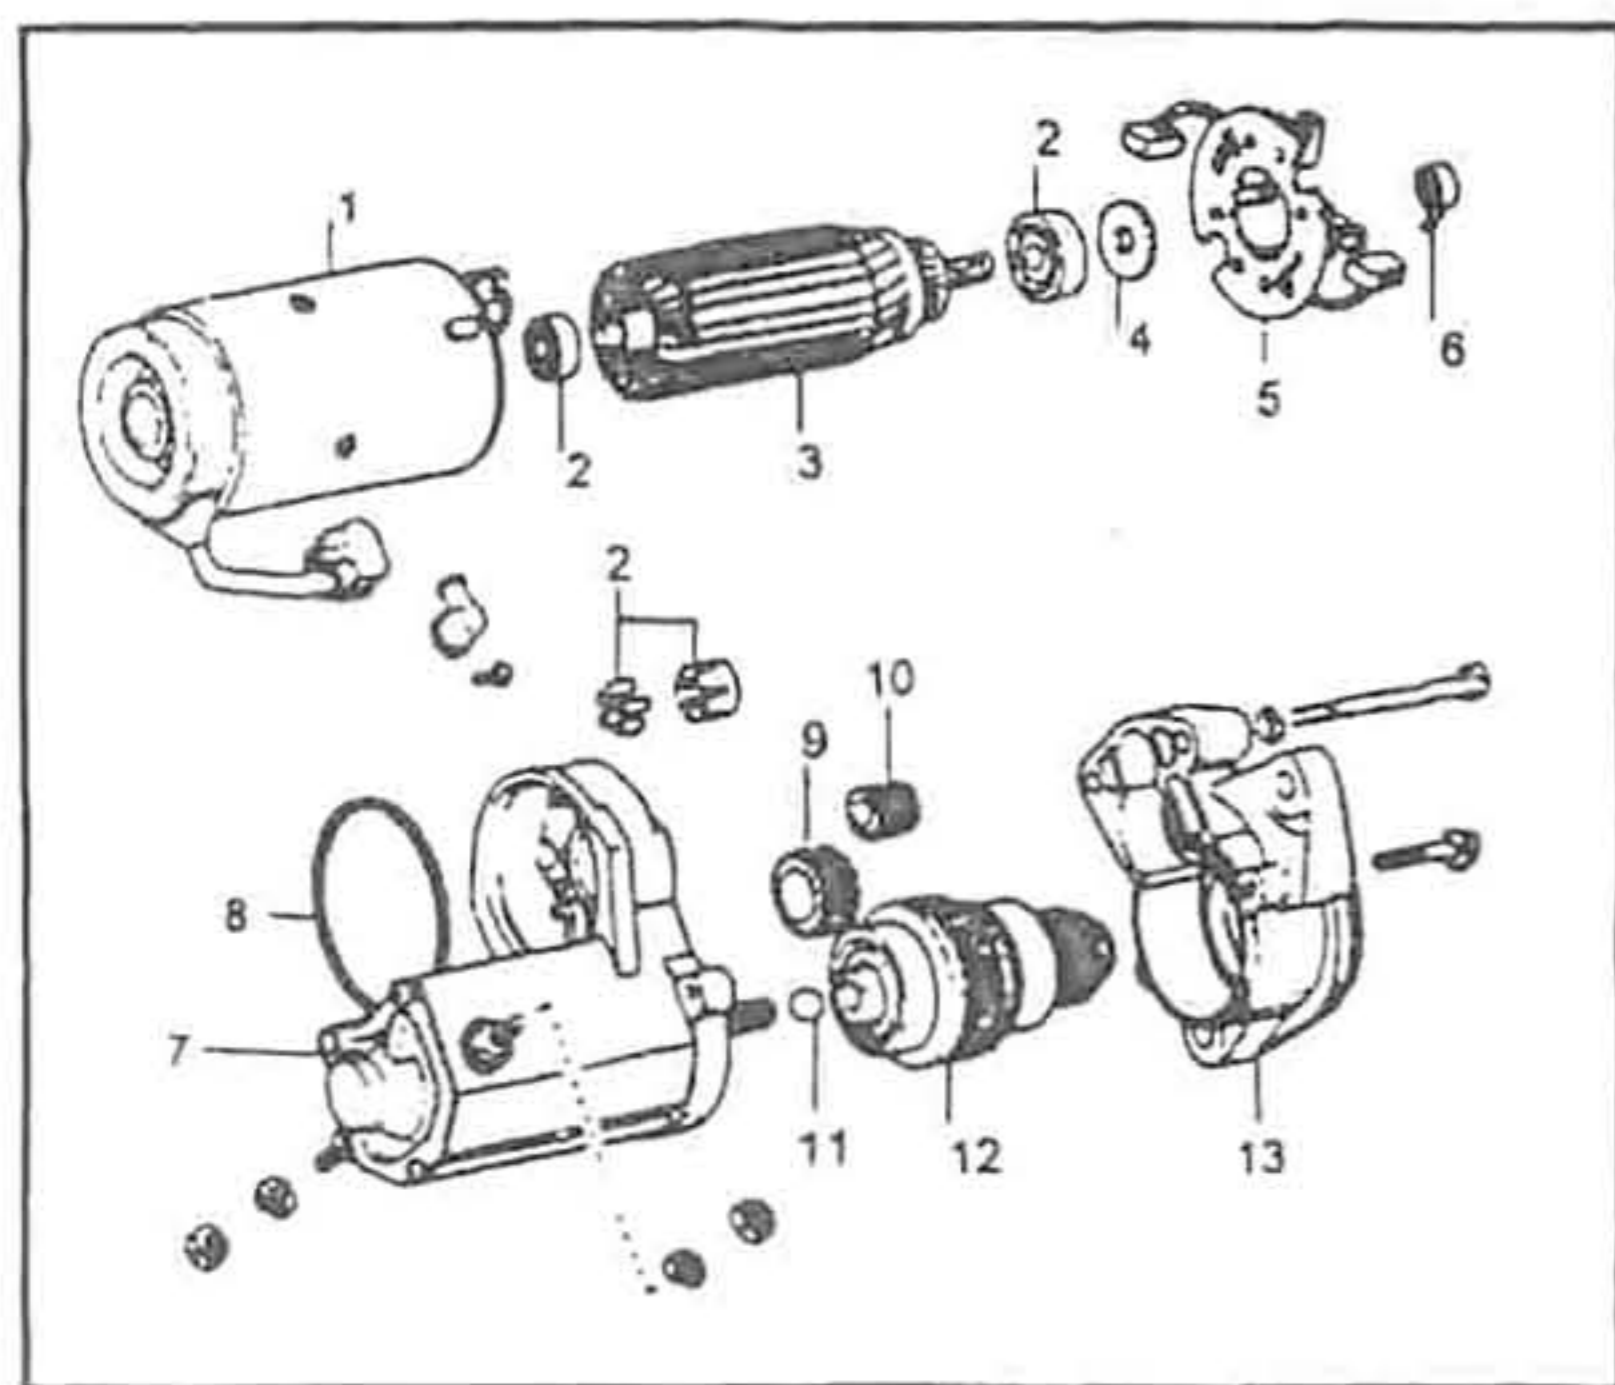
1. Корпус. 2. Подшипник. 3. Ротор. 4. Войлочное уплотнение. 5. Щеткодержатель. 6. Пружина щетки. 7. Корпус магнитной муфты. 8. Уплотнительное кольцо. 9. Промежуточная шестерня. 10. Шестерня. 11. Стальной шарик. 12. Муфта. 13. Крышка.
